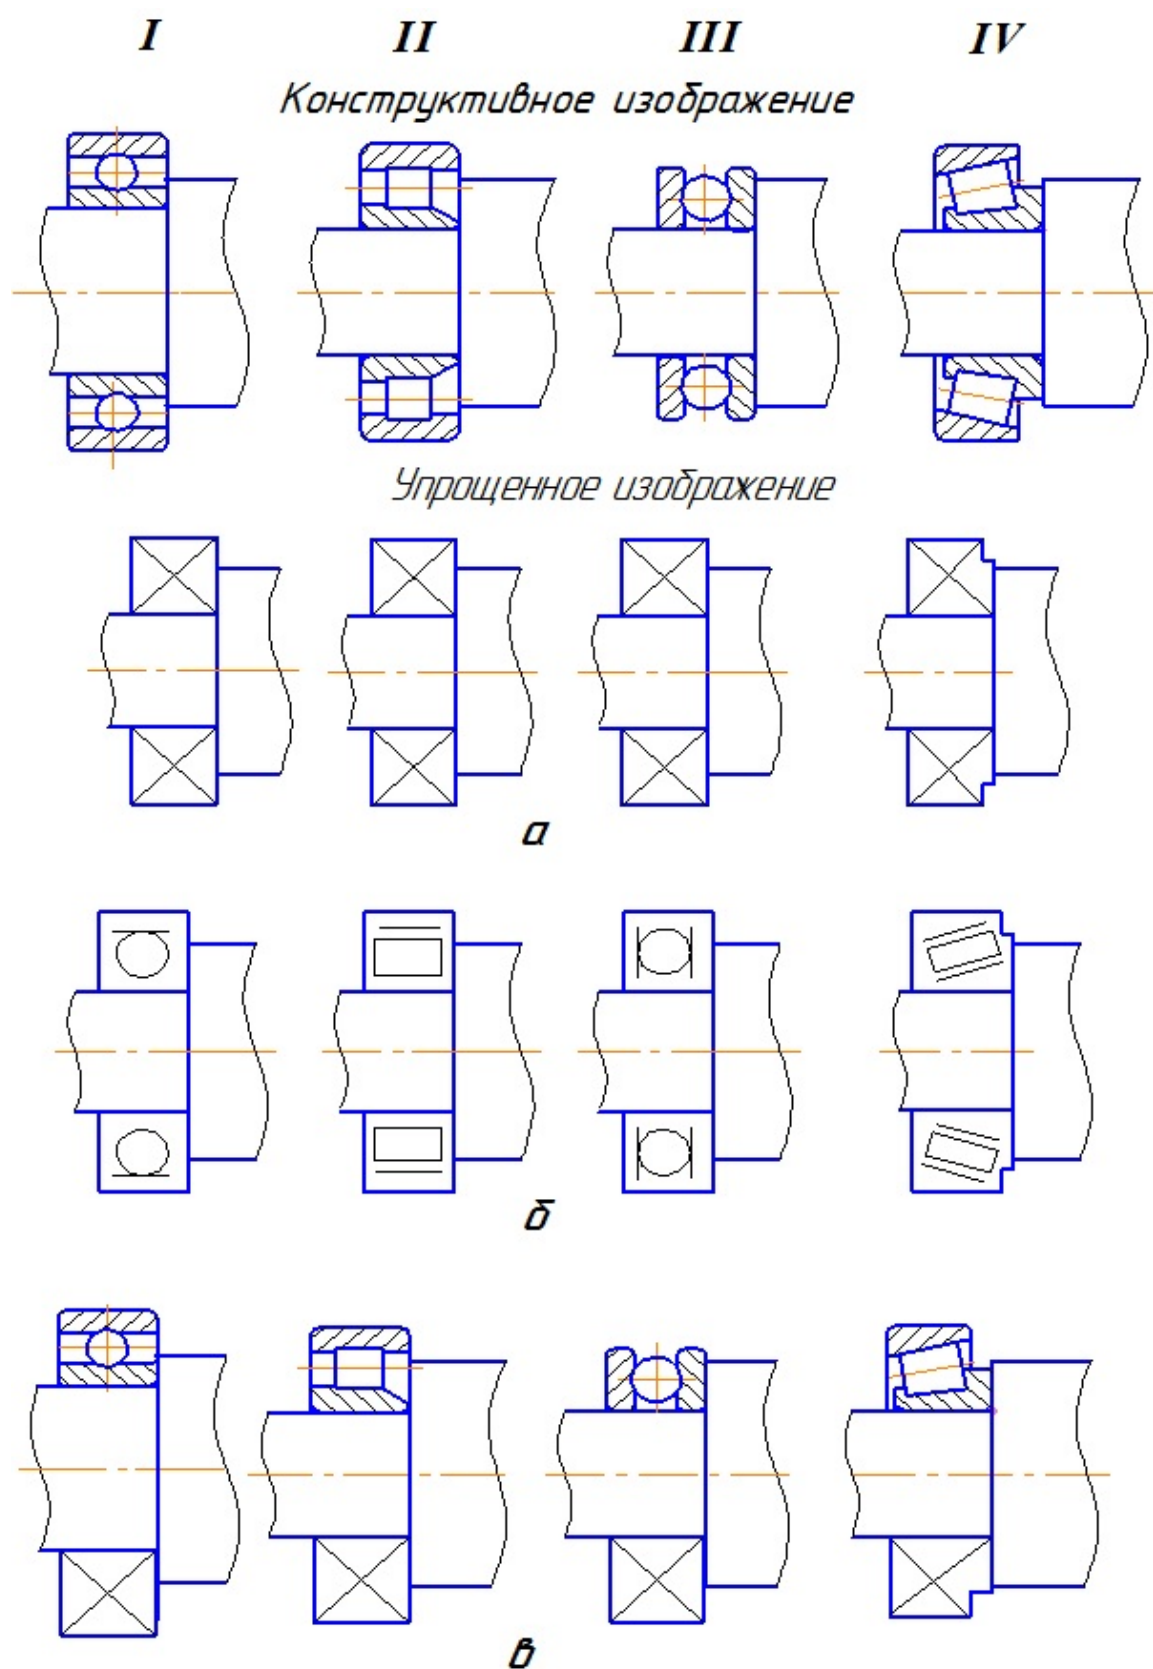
Изображения подшипников на чертежах и схемах:
